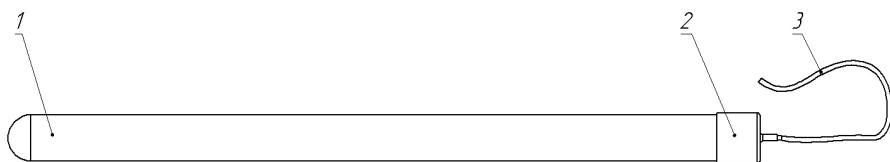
Схема конструкции АЗ.РСЗ.ФС.П
